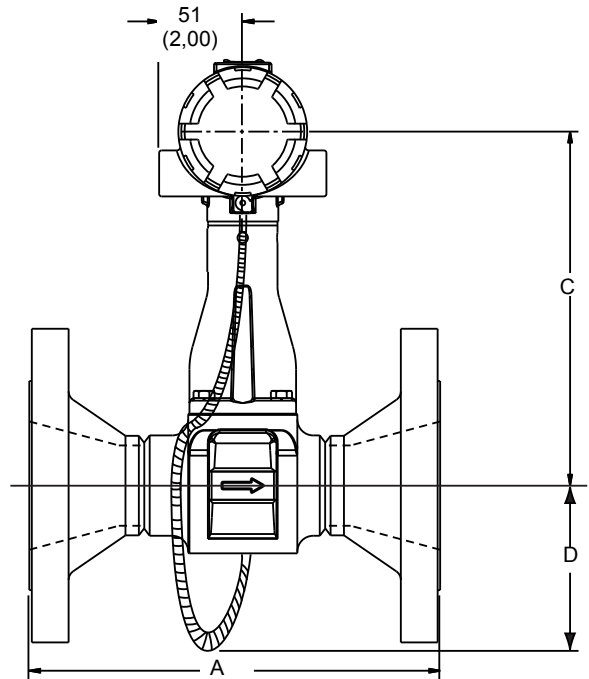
Габаритные чертежи расходомеров Rosemount 8800DR с коническими переходами (DN 25 - 300 мм/1 - 12 дюймов)
